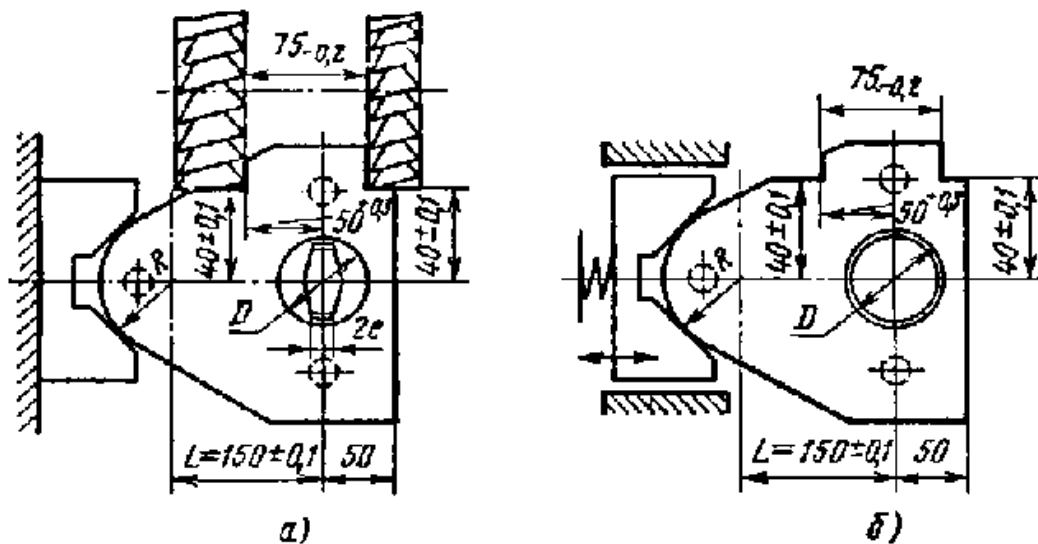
Схемы установки заготовки при фрезеровании (к задаче 7)
